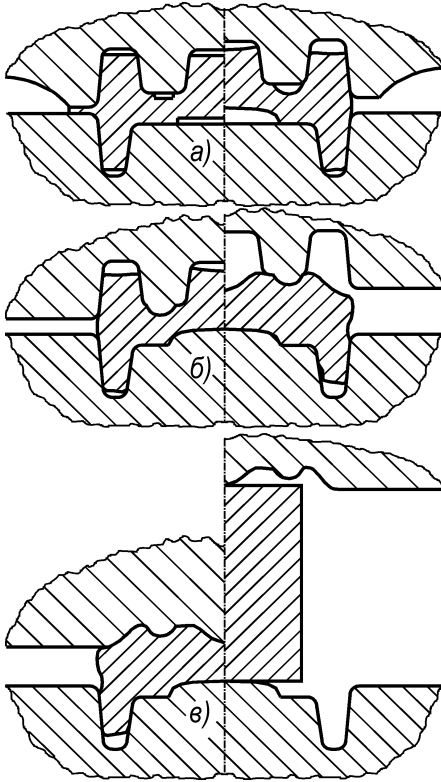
Схемы переходов оптимального варианта штамповки из заготовки $\varnothing 25$ мм, согласно цепочке 1-4-29: чистой (а), черновой (б) и заготовительный (в)
